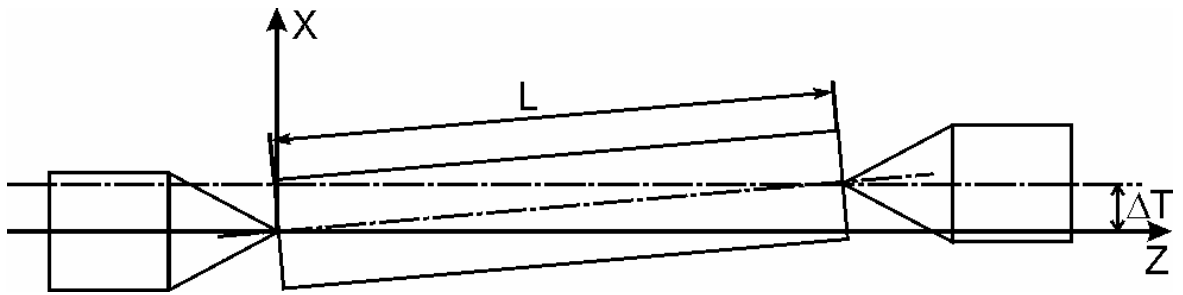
Схема для расчета погрешности установки заготовки в центрах
